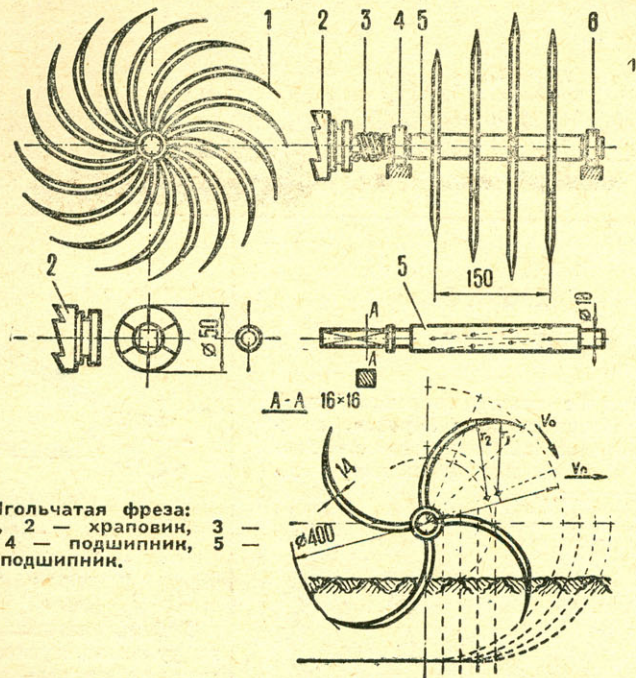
Игольчатая фреза: 1 — игла, 2 — храповик, 3 — пружина, 4 — подшипник, 5 — вал, 6 — подшипник.
